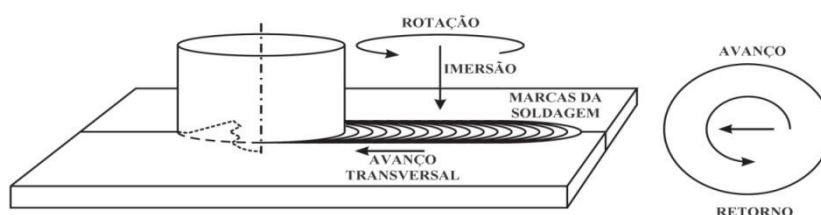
Esquemática da soldagem por fricção linear (Fonte: Centeno, 2008).
